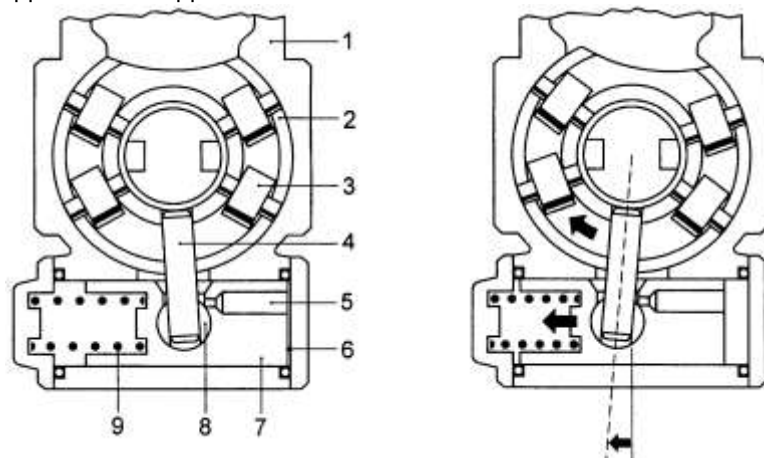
Схема регулирования УОВТ в ТНВД VE: слева-исходное положение, справа - при повышении давления подкачки; 1 - корпус; 2 - кольцо; 3 - ролик; 4 - шток; 5 - канал в поршне; 6 - рабочая полость гидроцилиндра; 7 - поршень; 8 - шарнир; 9 - возвратная пружина.
